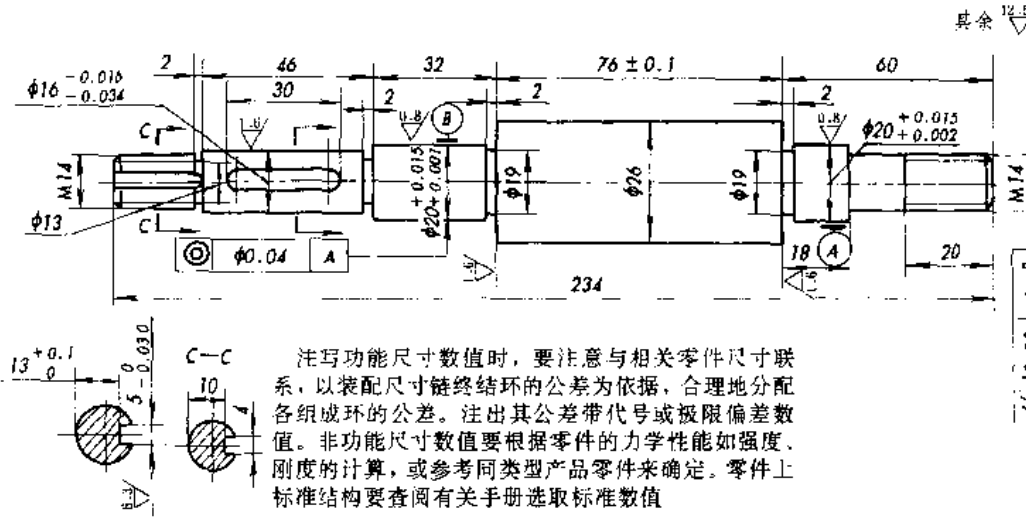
形位公差和尺寸公差分开注写
